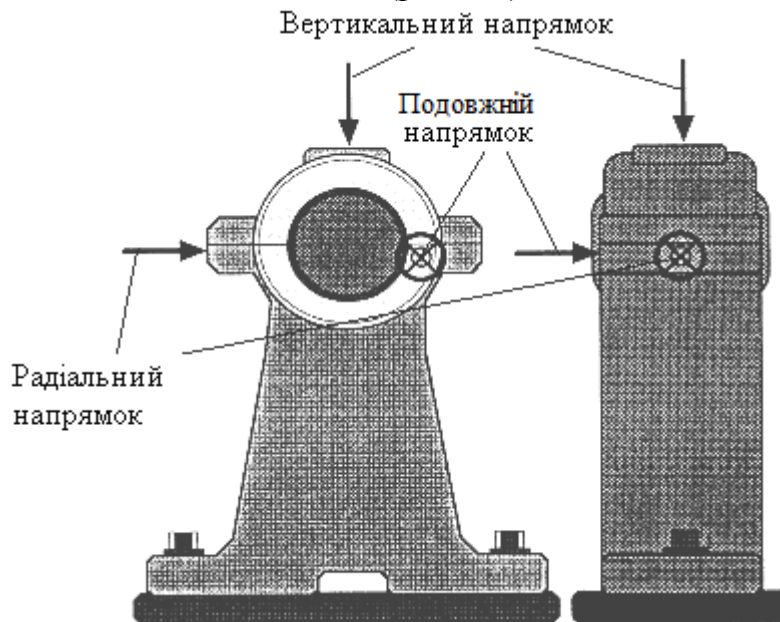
Контрольні точки вимірювань вібрації на корпусі підшипникових опор ротора
